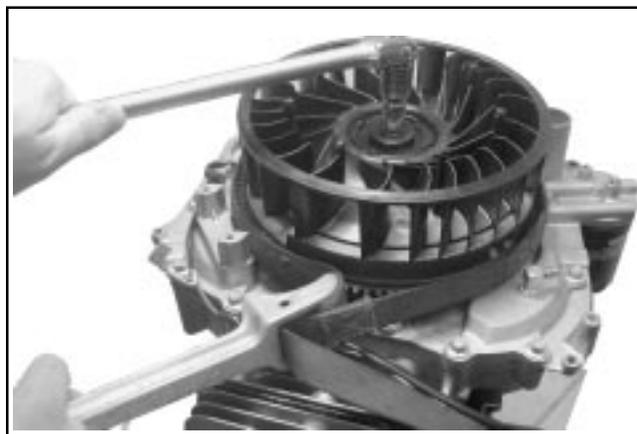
Dépose du ventilateur et des éléments de montage du volant.
